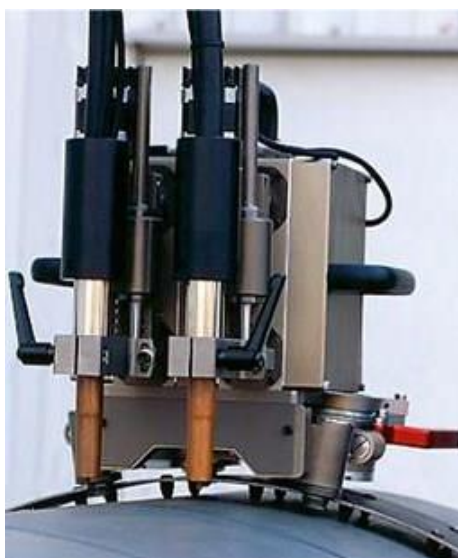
Сварка двухдуговой головкой Р-600
